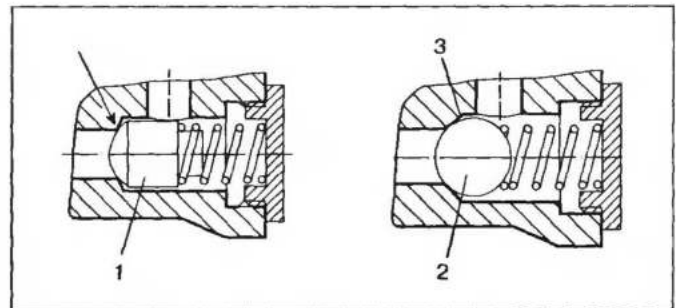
Ремонт редукционного клапана системы смазки с заменой цилиндрического клапана на шариковый:
